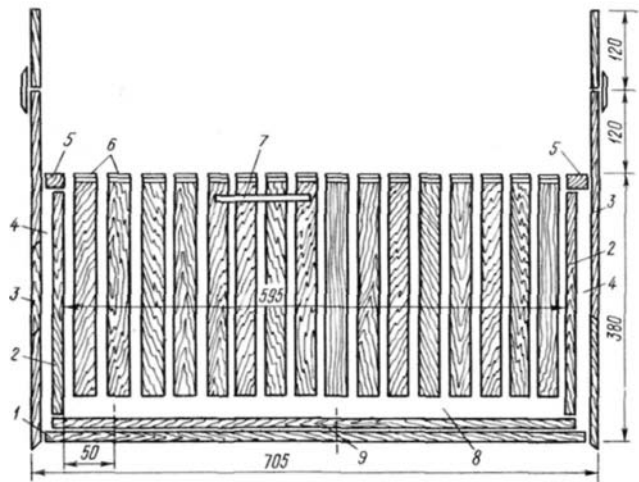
Схема улья в разрезе от передней стенки поперек рамок;
